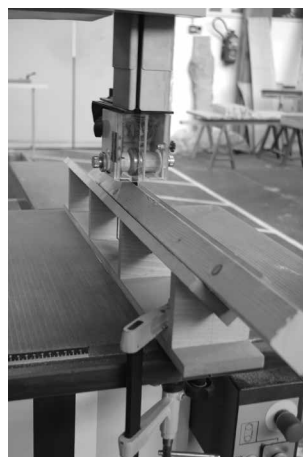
Sciage avec montage d'usinage pour coupe à 45 °
